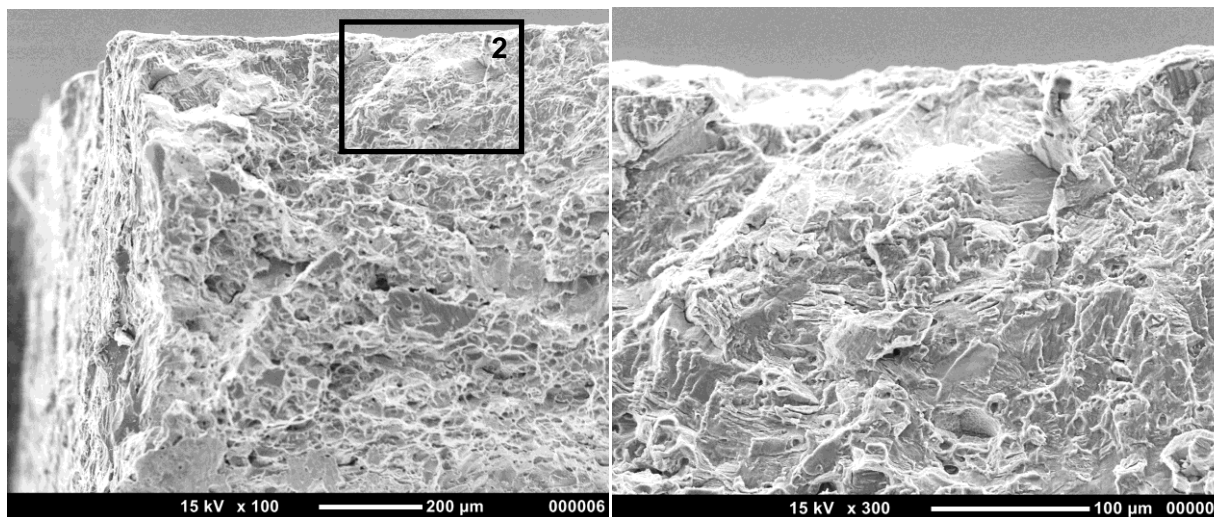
Übersichtsaufnahme der Bruchoberfläche einer Schweißung des Parametersatzes IMWF-33-00020 ($n=1500 \text{ min}^{-1}$, $v_x=500 \text{ mm/min}$)
